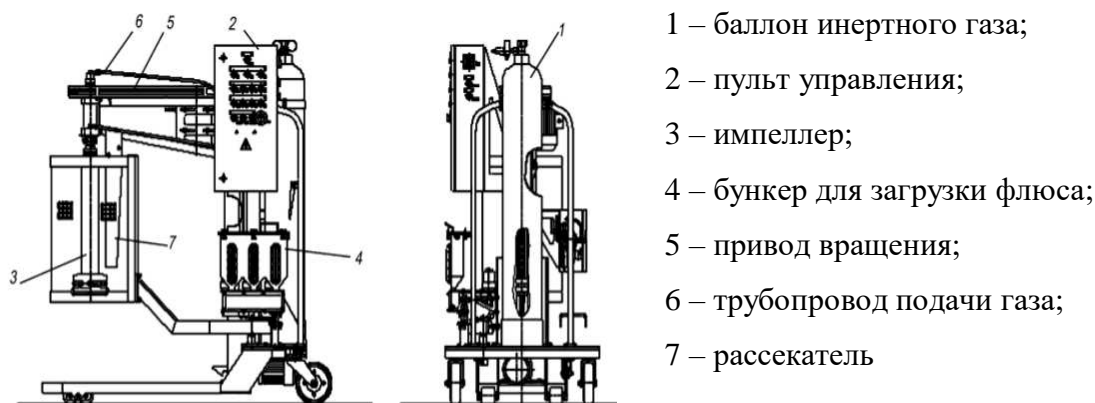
Схема установки продувки расплава П1873.00.000
